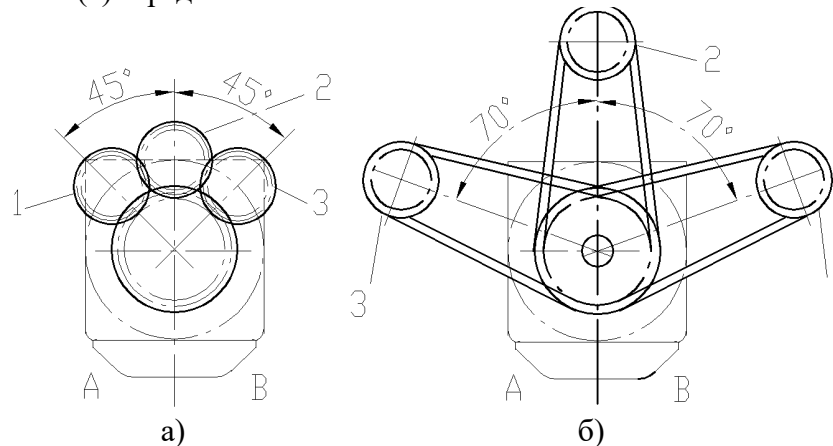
Схема выбора оптимального угла установки зубчатой (а) и клиноременной (б) передачи (Вид со стороны вала).
